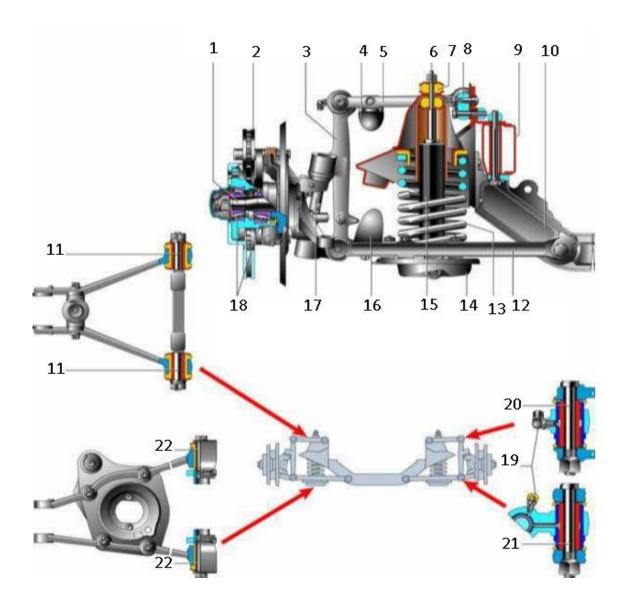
Схема передней шкворневой подвески: 1 — цапфа поворотного кулака; 2 — тормозной диск; 3 — стойка; 4 — буфер отбоя; 5 — верхний рычаг; 6 — шток амортизатора; 7 — подушки верхнего крепления амортизатора; 8 — ось верхнего рычага; 9 — лонжерон; 10 — балка; 11 — резинометаллические шарниры верхнего рычага; 12 — нижний рычаг; 13 — пружина; 14 — чашка пружины; 15 — амортизатор; 16 — буфер сжатия; 17 — шкворень; 18 — роликовые подшипники ступицы колеса; 19 — пресс- масленки; 20 и 21 — резьбовые втулки стойки; 22 — резинометаллические шарниры нижнего рычага
